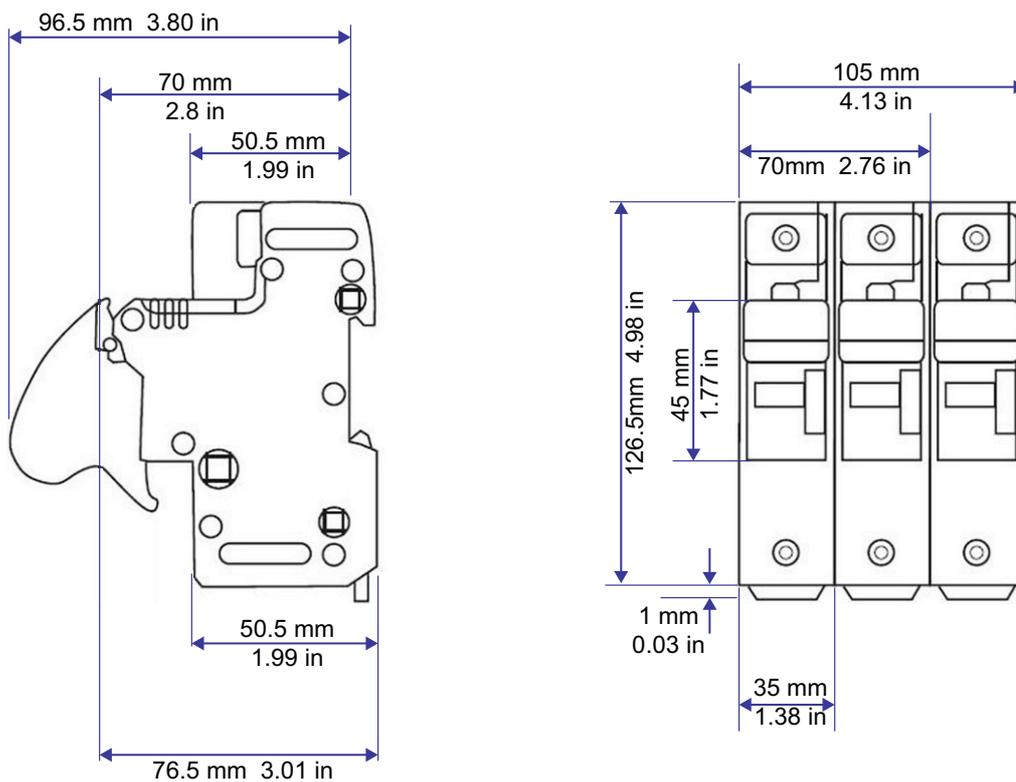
Dimensions du porte-fusible : US223 (22x58 mm)
